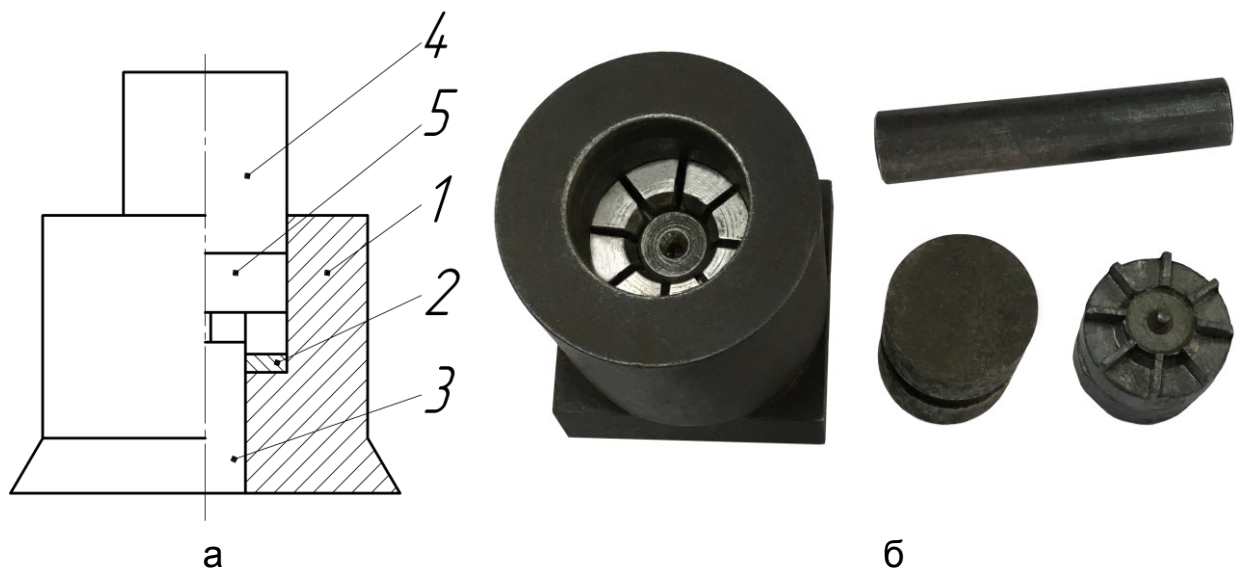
Конструкція експериментального штампа для закритого штампування (а) і загальний вигляд штампа, заготовки й поковки (б); 1 – корпус; 2 – матриця; 3 – виштовхувач; 4 – пуансон; 5 – заготовка
